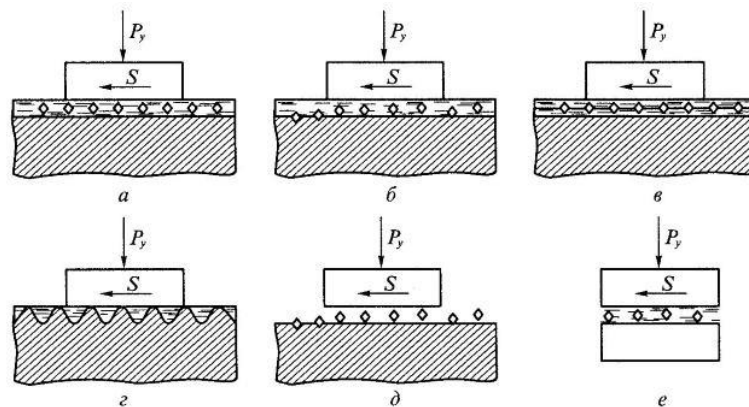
Схеми притирання металевих поверхонь:
